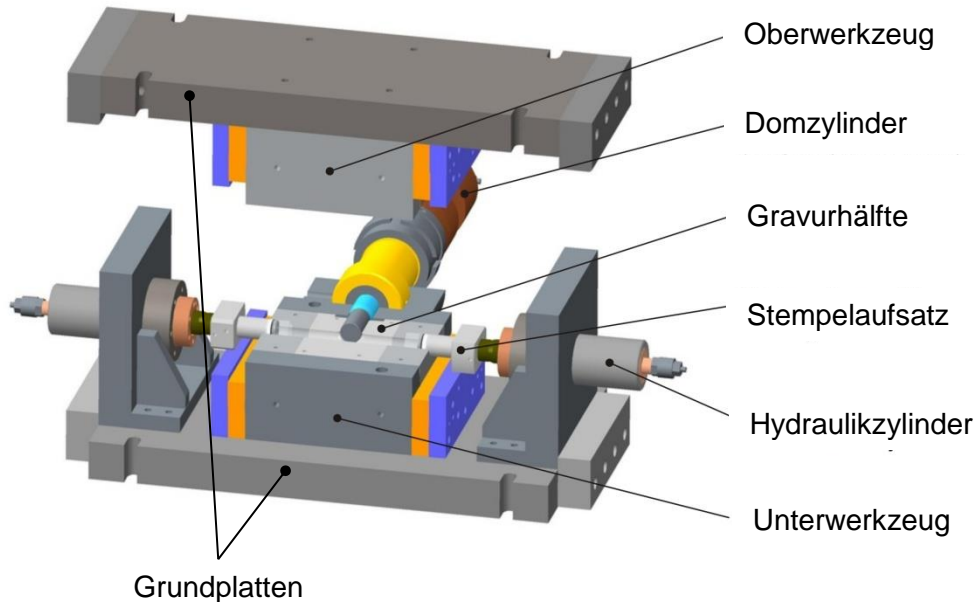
IHU-Werkzeug zum Einbau in hydraulischer Presse (Bildquelle: IPH)
